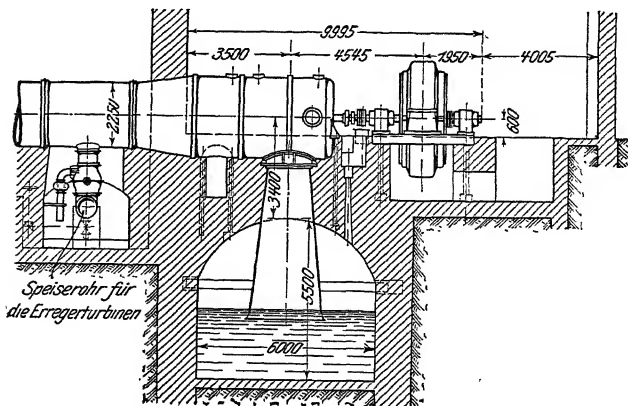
Kesselturbine mit axialem Einlauf (Frontalturbine).
